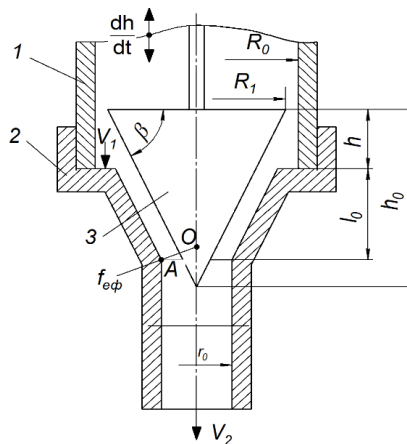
Розрахункова схема живильника адаптронного модуля дозування з конусним клапаном регулювання потоку рідкої продукції: 1 — мірний циліндр; 2 — насадка; 3 — конусний клапан
